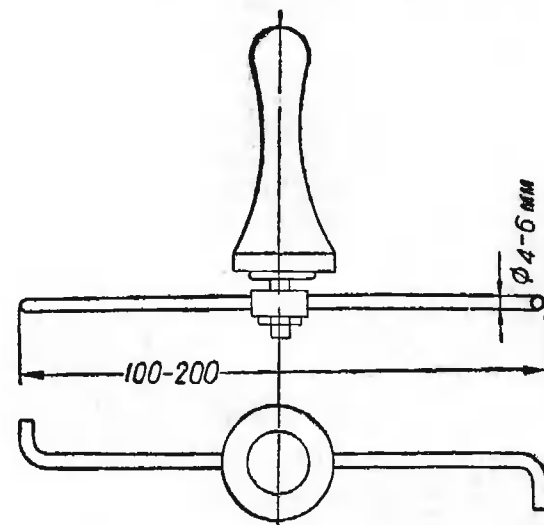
Вертушка для проверки наличия вращающегося магнитного поля статора.
